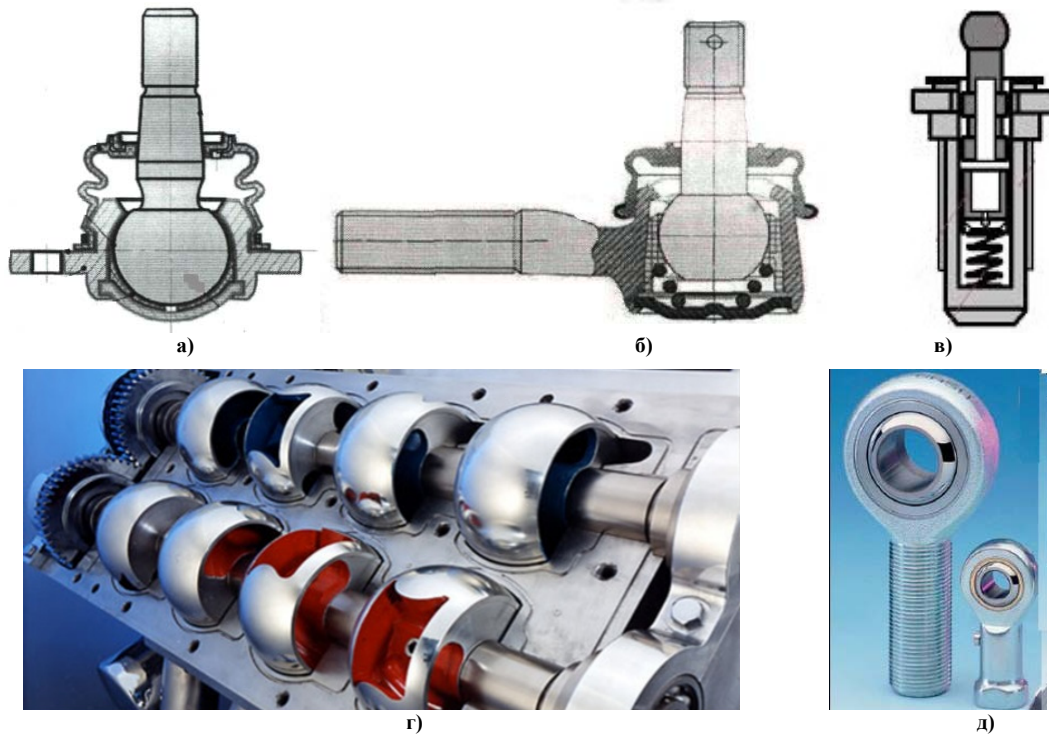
Характерні представники деталей з неповними сферичними поверхнями:
